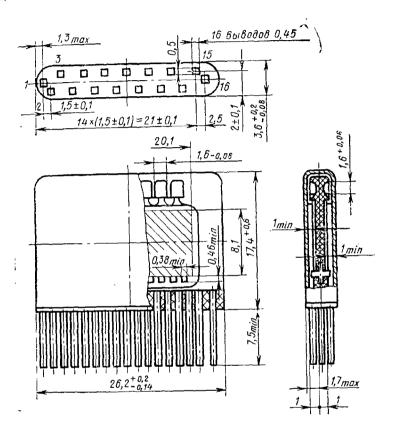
Конструкция металлополимерного корпуса «Пенал»
